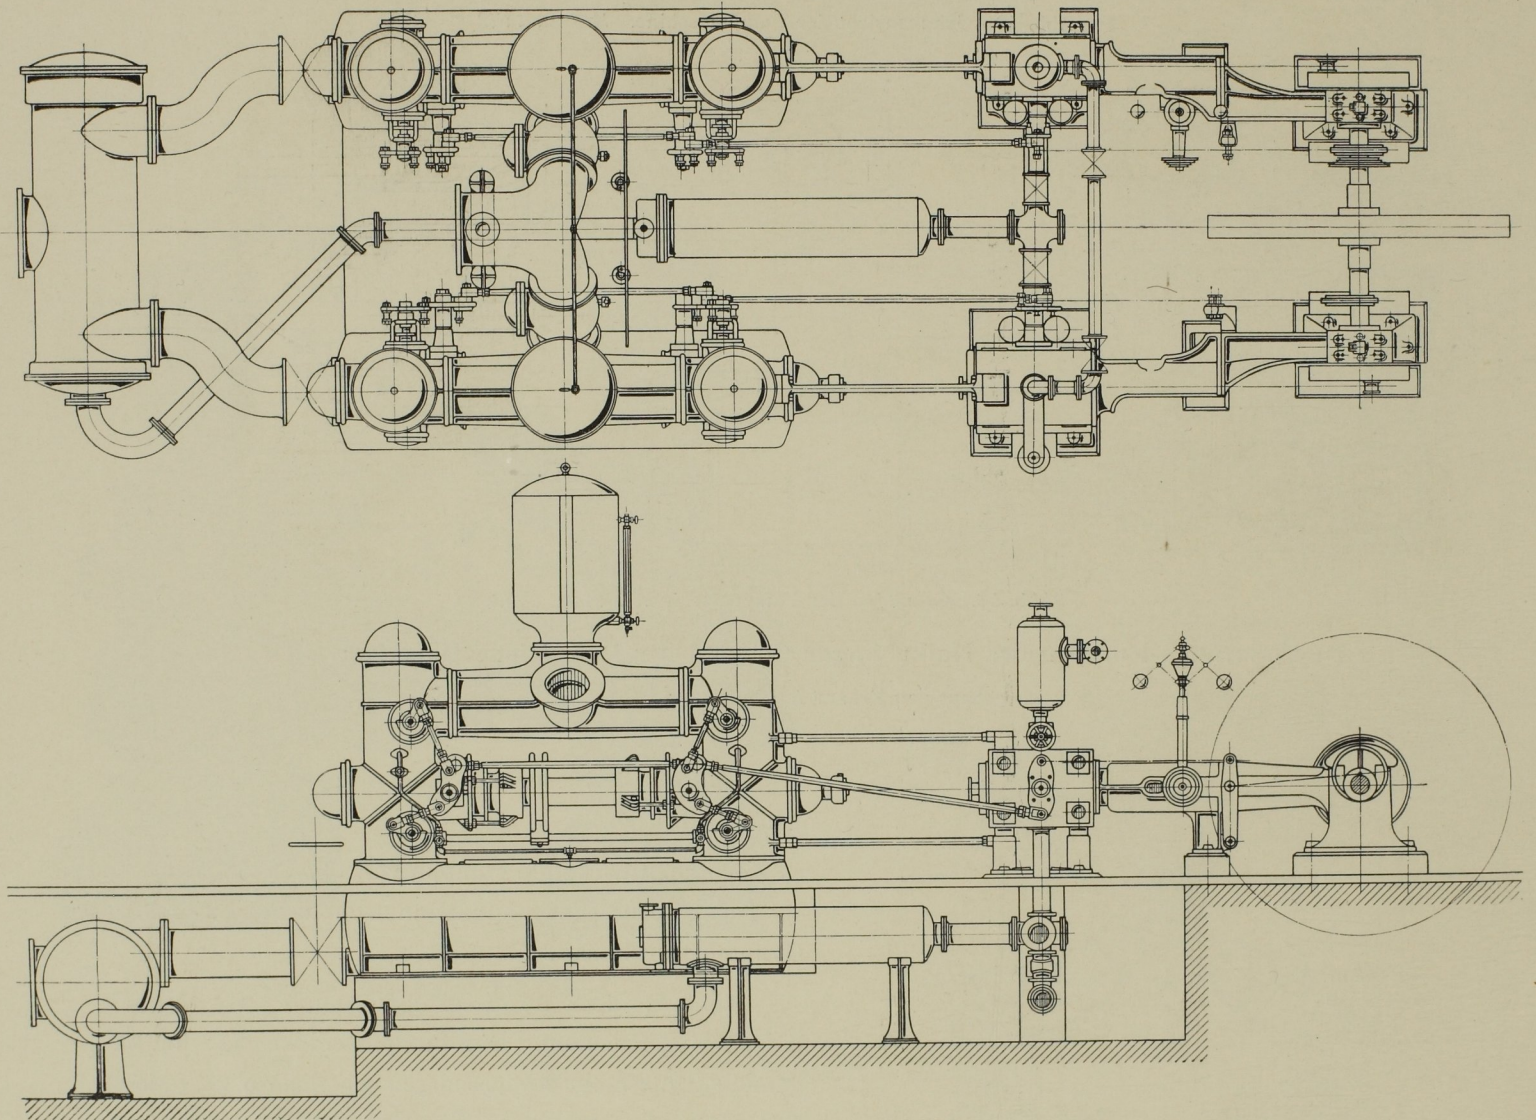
Grundriss und Seitenansicht der Pumpmaschine. [Massst. 1:64.
